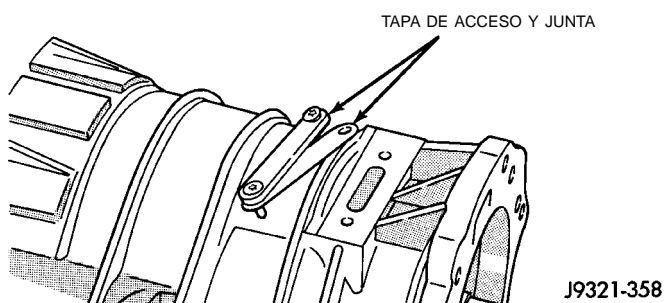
Desmontaje/instalación de la tapa de acceso y la junta
